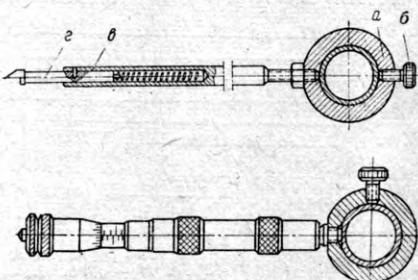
Указатель для измерения углов (вверху) и сменный нутромер (внизу)
